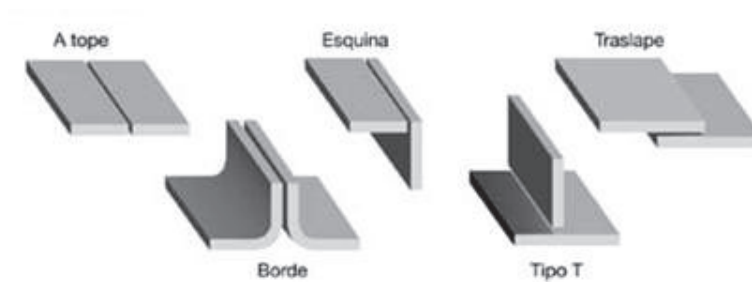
26 Conexiones de perfiles y planchas por soldadura¹⁷
